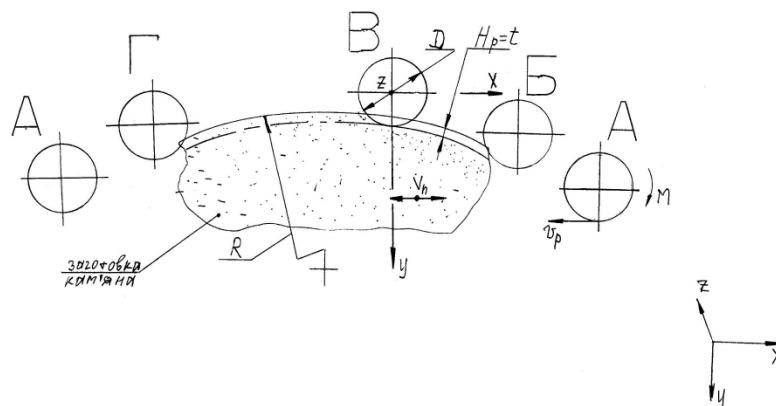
Схема етапів технологічного процесу фрезерування (шліфування) кам'яної заготовки алмазним профільним роликом АПР (вид у плані):
